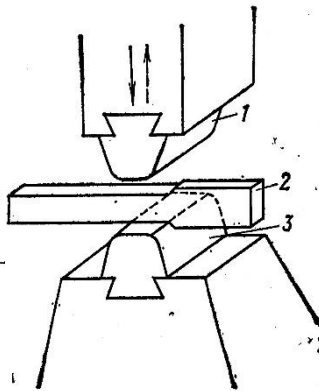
Схема процесса свободнойковки: 1-верхний боек; 2-обрабатываемая заготовка; 3- нижний боек
